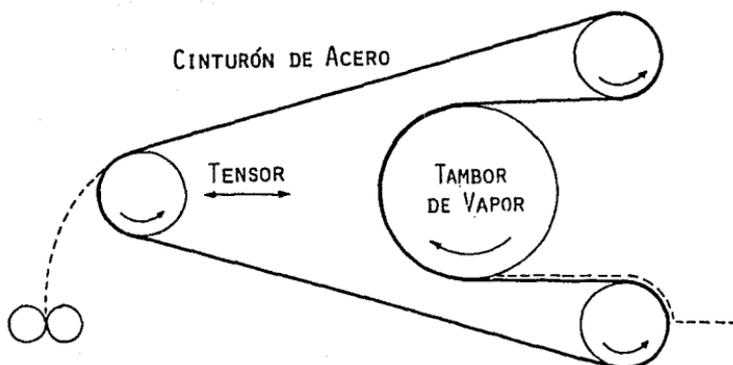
,3 MÉTODO DE CURADO POR TAMBORES
